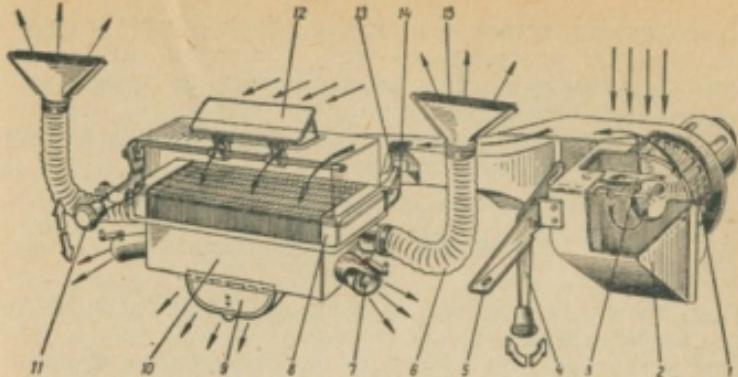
Схема системы отопления и обдува ветрового стекла:
